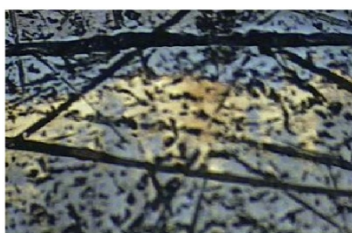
Поверхня деталі, на якій наведені послідовні ділянки «сталь – бронза після наступної механічної обробки (риски на фото – сліди абразивних зерен)
